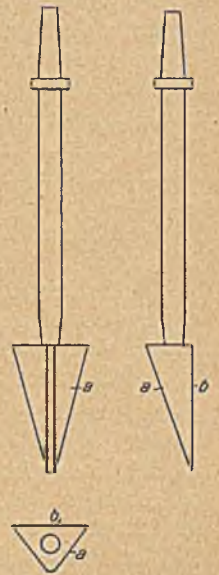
Neues Keilwerkzeug der Fried. Krupp A.G. für Abbauhämmer.
